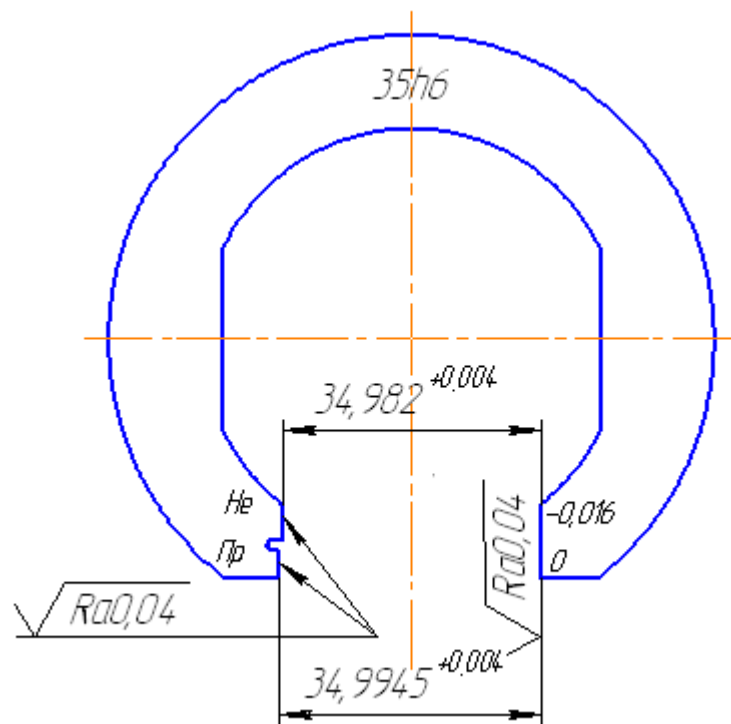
Калибр-скоба для контроля вала $\varnothing 35h6$
